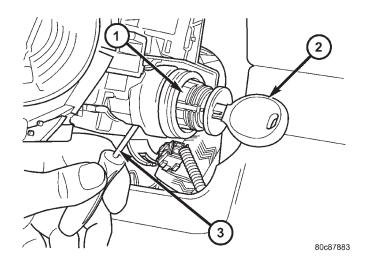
DESENGANCHE DEL CILINDRO DE CERRADURA
